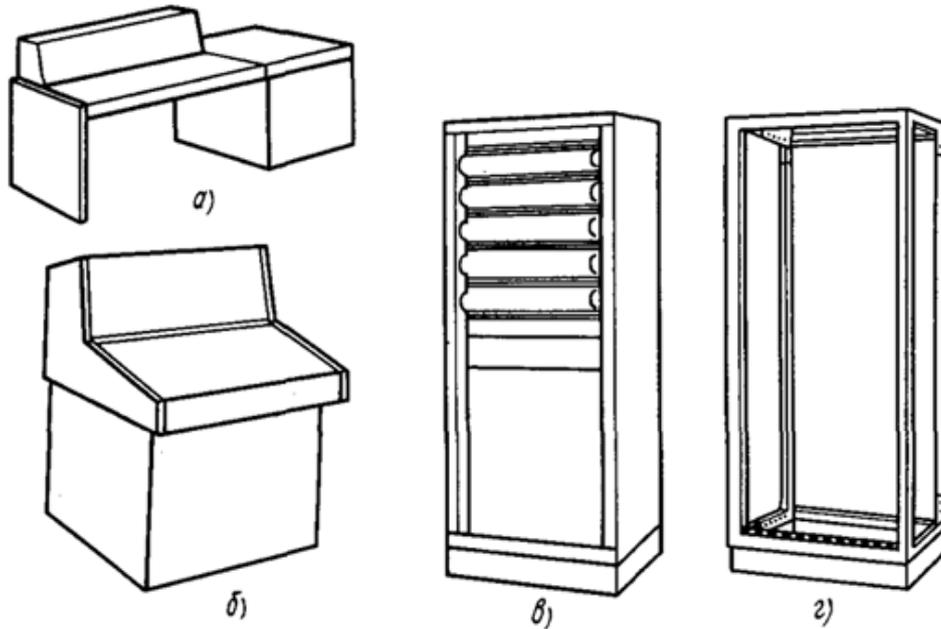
Схема конструкций частичных корпусов комплекса универсальных типовых конструкций УТК [3, 5]:
